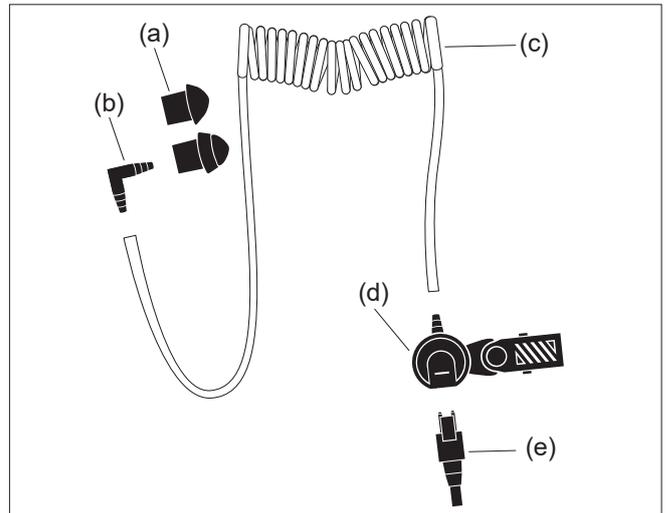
Explosionszeichnung des Akustikschlauchs
